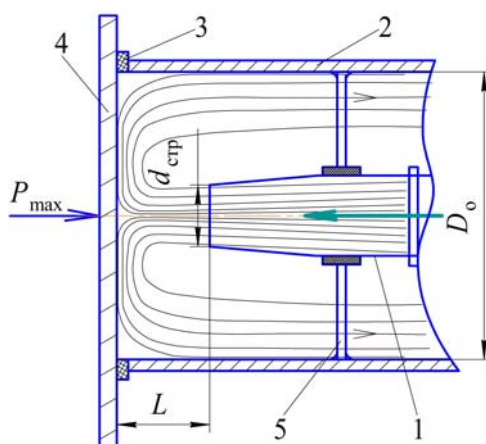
Схема струйного устройства для реализации процесса реверсивно-струйной очистки
